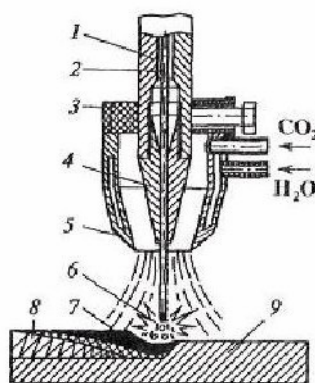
Схема наплавки в среде углекислого газа: 1 – мундштук; 2 – электродная проволока; 3 – горелка; 4 – наконечник; 5 – сопло горелки; 6 – электрическая дуга; 7 – сварочная ванна; 8 – наплавленный валик; 9 – восстанавливаемое изделие
